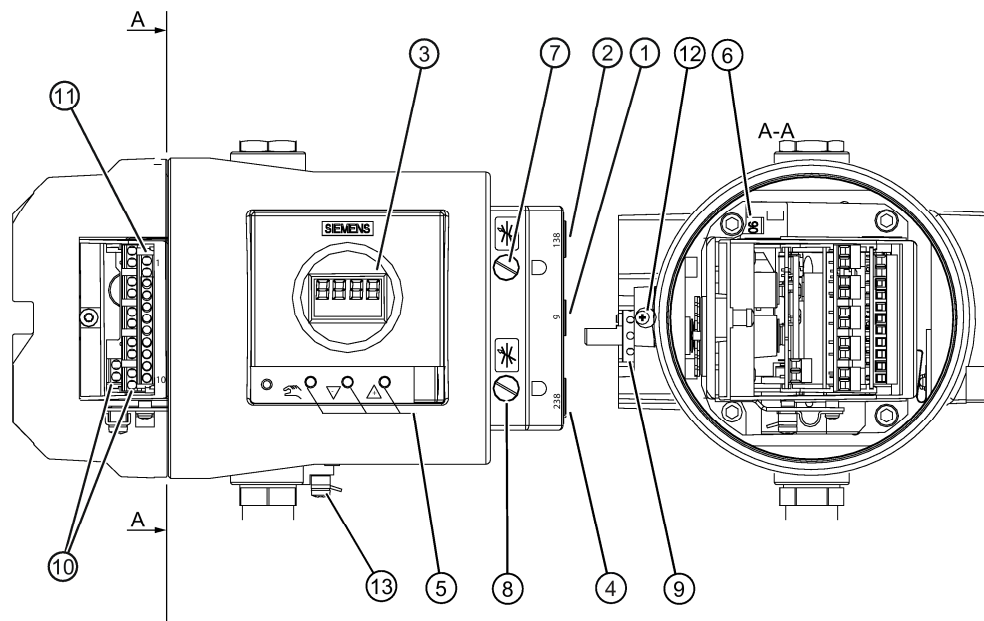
Внешний вид позиционера (с открытой крышкой: корпус из макролона)
